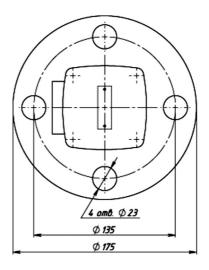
Габаритные и установочные размеры акустического датчика. Для контроля одного уровня.
